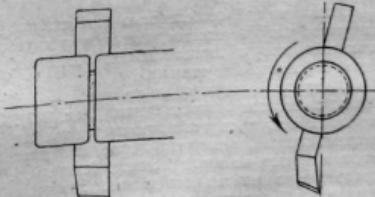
Схема фрезеровки зуба анкерного колеса.
